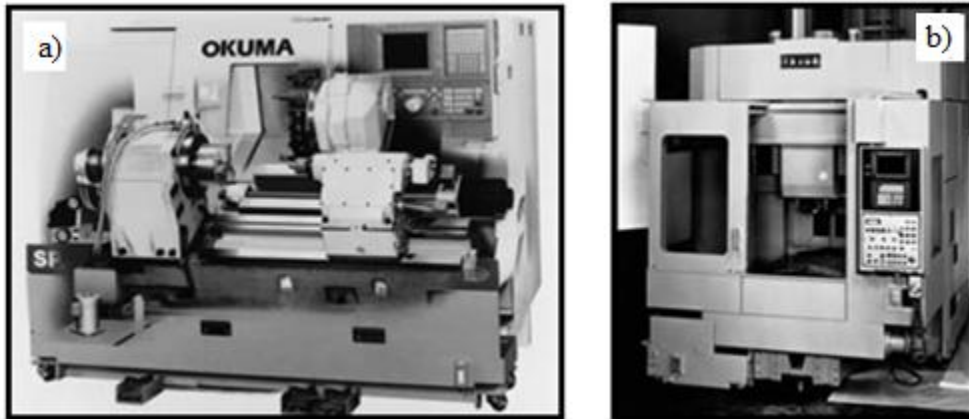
Máquinas-herramienta de control numérico. a) Torno, b) Fresadora.
